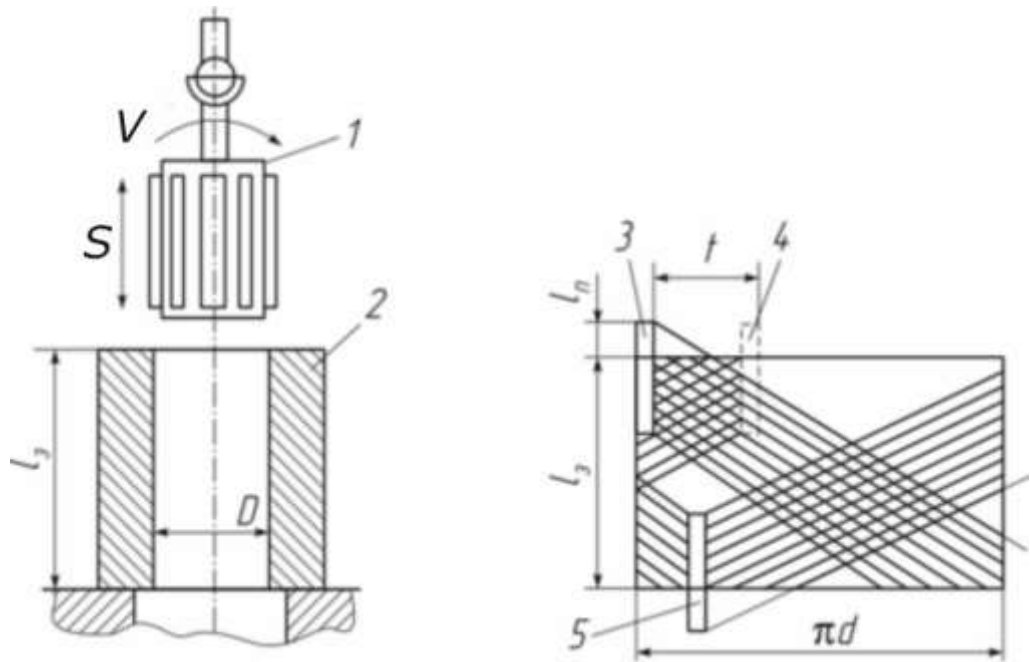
Схема роботи хонінгувальної головки: 1 хона; 2 – заготовка; 3,4,5 – положення хонінгувальних брусків у процесі обробки.
